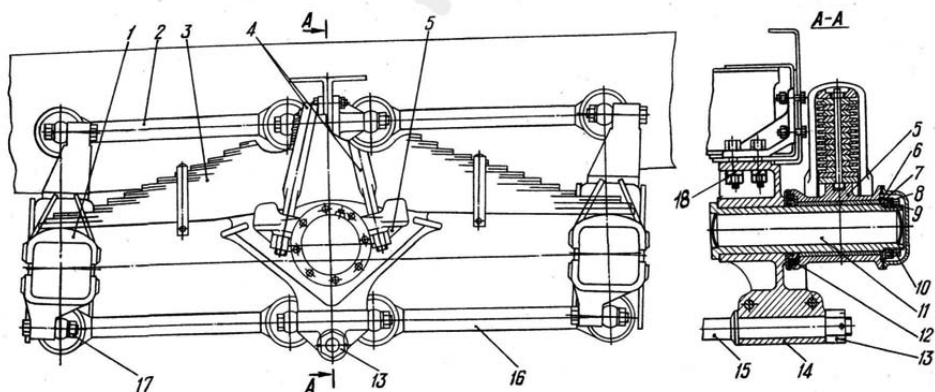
Задняя подвеска трехосных автомобилей: 1 — опора; 2, 16 — штанги реактивные; 3 — рессора; 4 — стремянки; 5 — балансир; 6 — кольцо упорное; 7 — гайка кольцевая; 8 — шайба стопорная; 9 — шайба замковая; 10 — контргайка; 11 — ось балансира; 12 — сальник; 13, 17, 18 — гайки; 14 — кронштейн; 15 — стяжка
